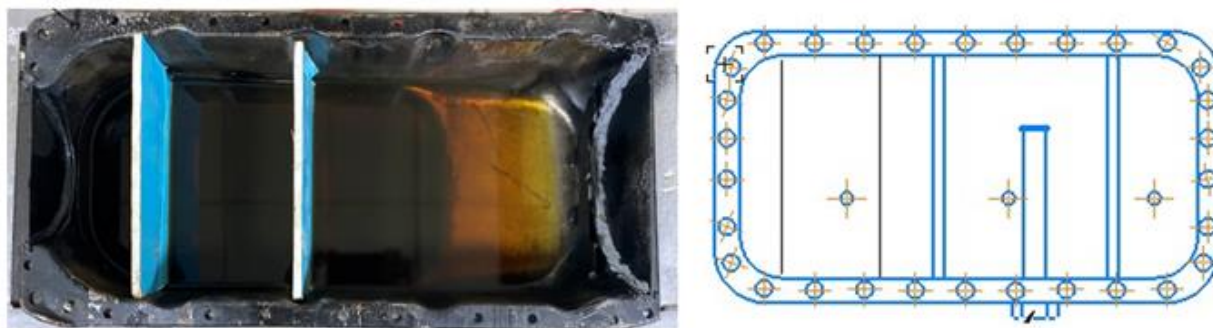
Модернизированный картер двигателя Д-243 с установленными дополнительными перегородками
